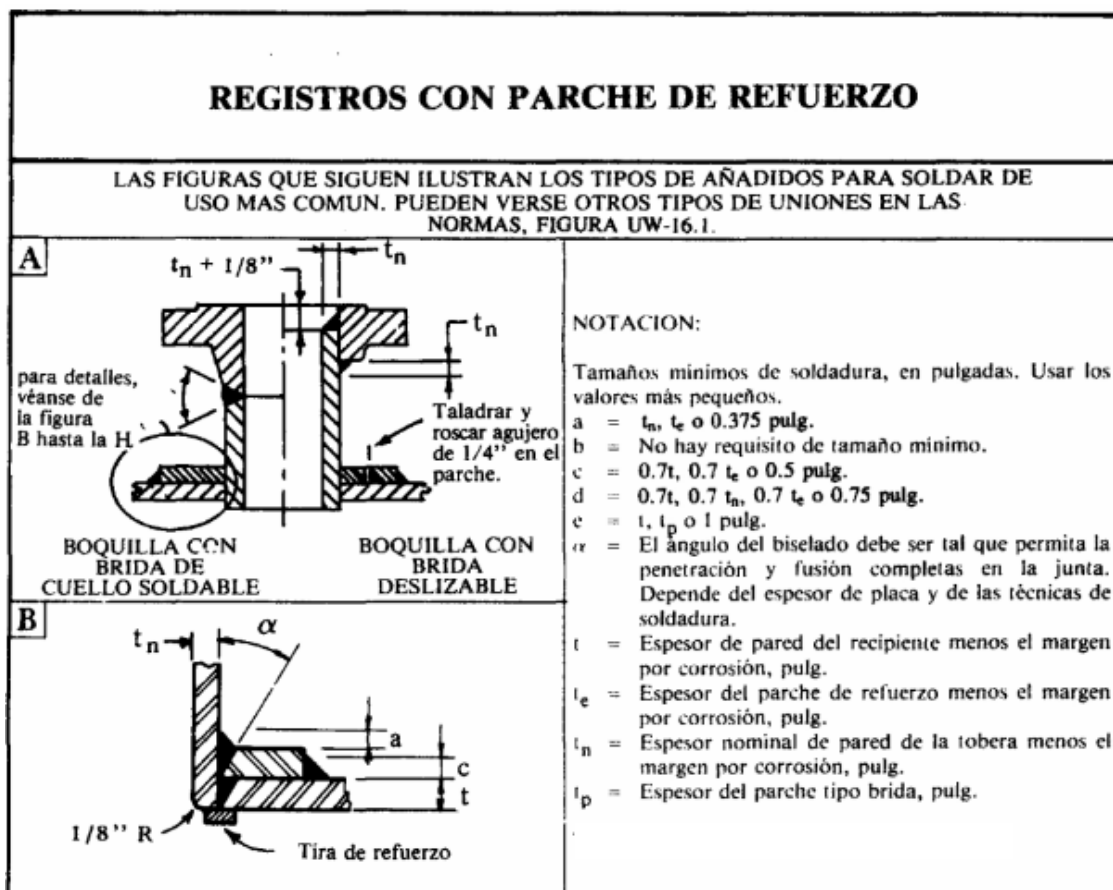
Soldadura de tubuladura (con brida de cuello soldable) con parche de refuerzo.
